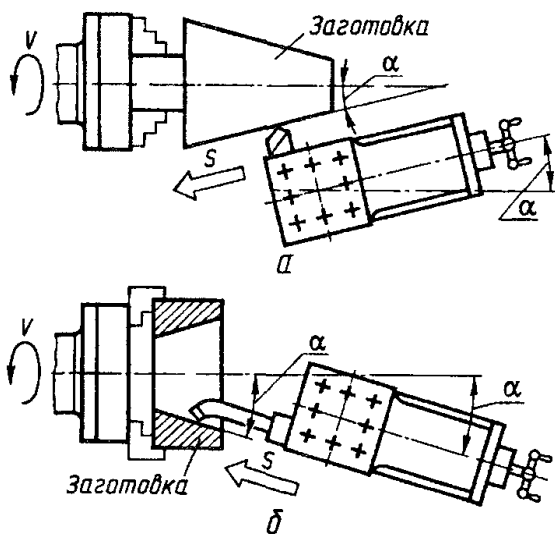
Обробка конічних поверхонь за повернутих верхніх полозків супорта:
